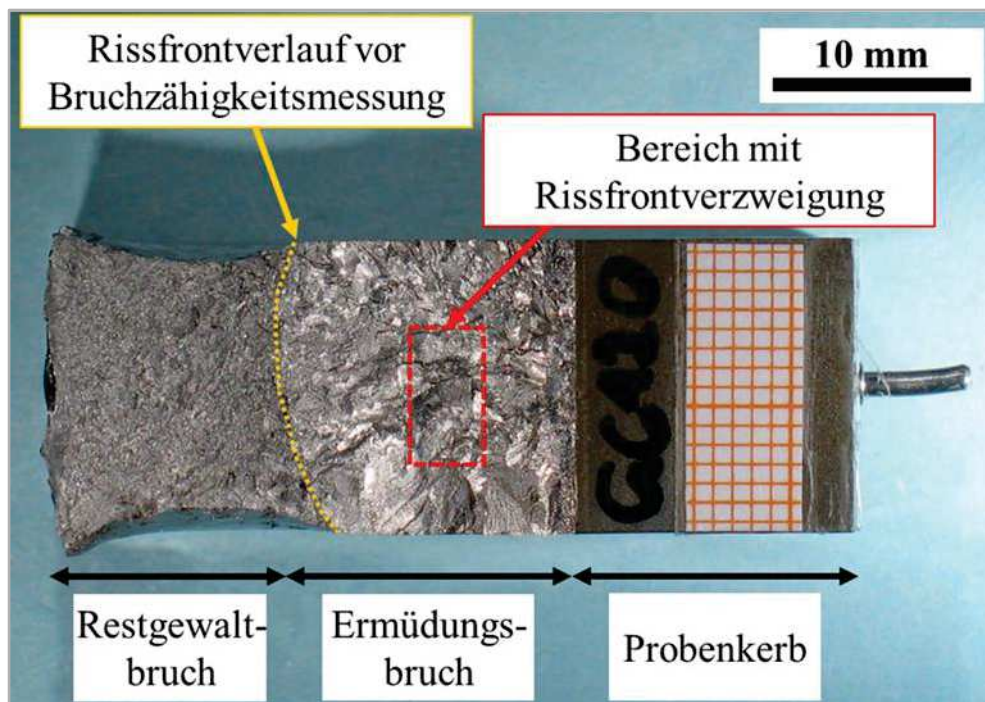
Aufsicht auf die Bruchfläche der GCMn1.20-Probe
